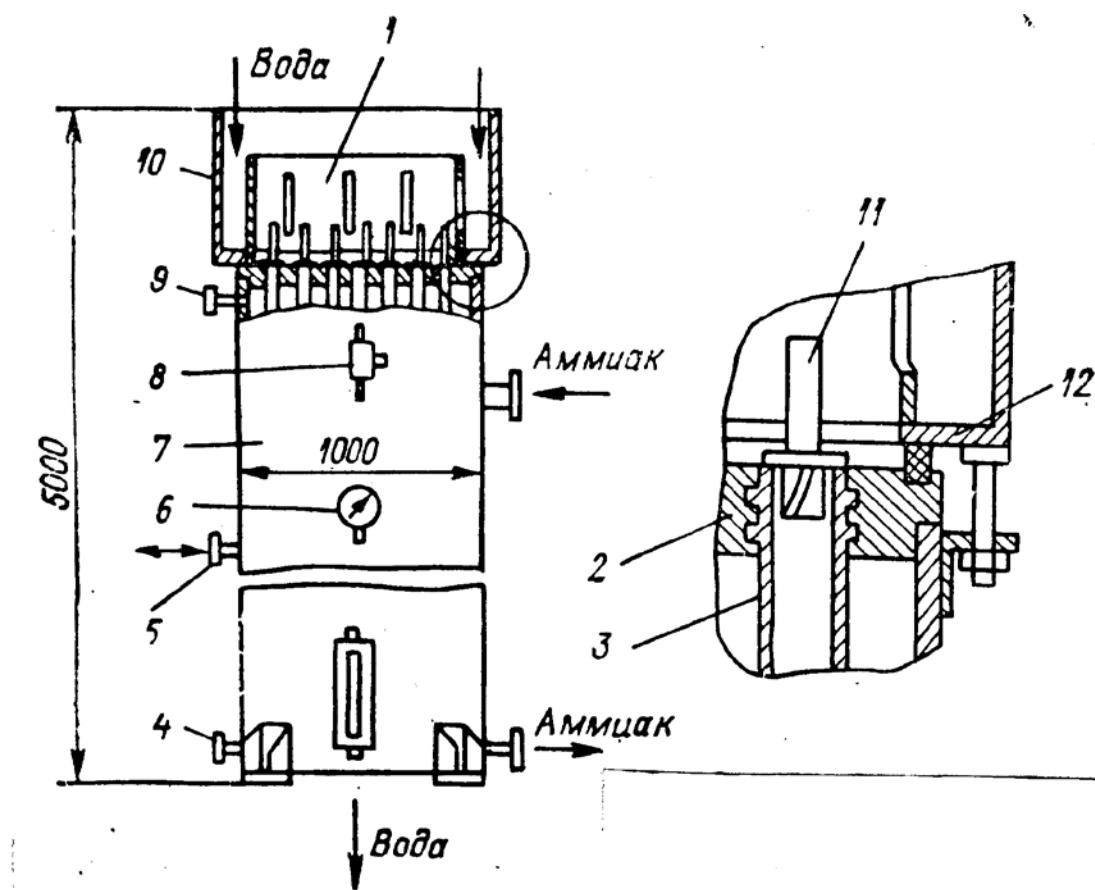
Вертикальний кожухотрубний конденсатор.
